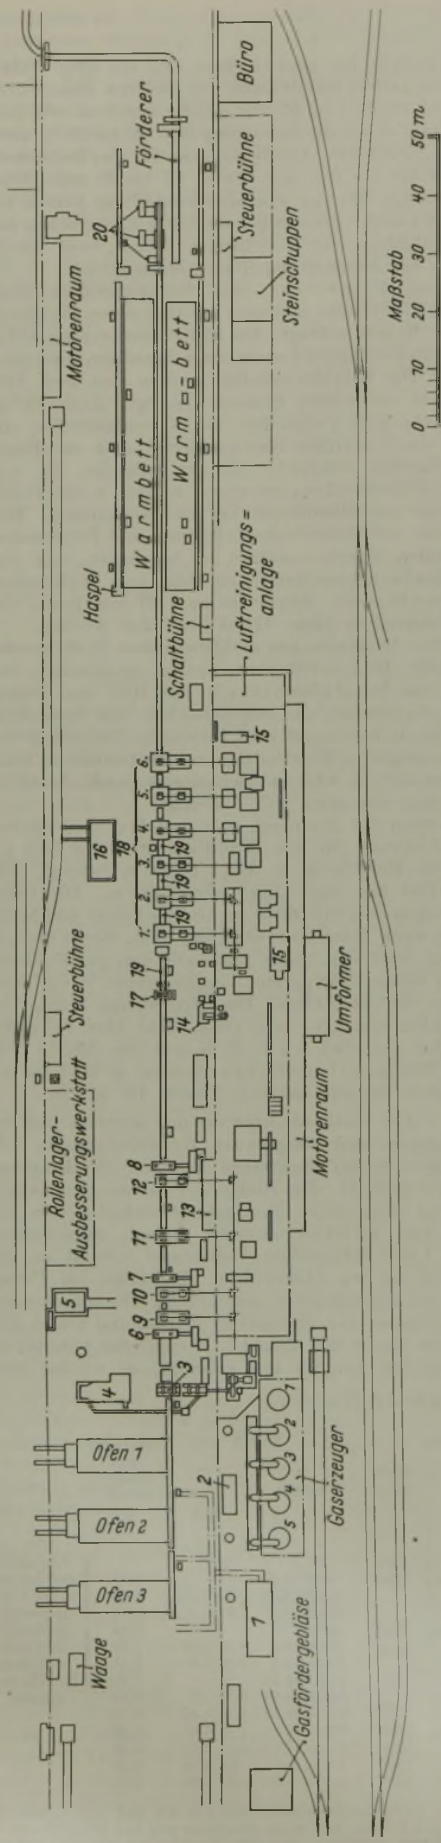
Grundriss der Bandblech-Walzwerksanlage der Republic Steel Corporation.
